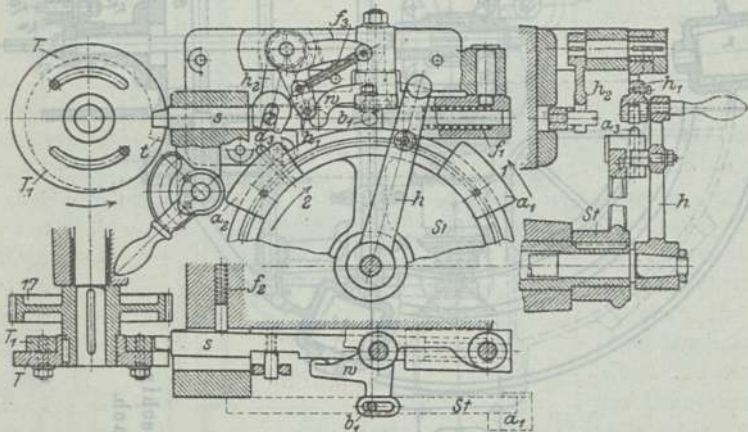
bis 650. Steuerung der Werkzeugschleifmaschine.
